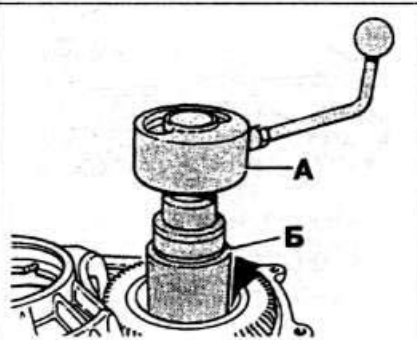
Проверка момента сопротивления подшипников проворачиванию ведущей вал-шестерни главной передачи:
